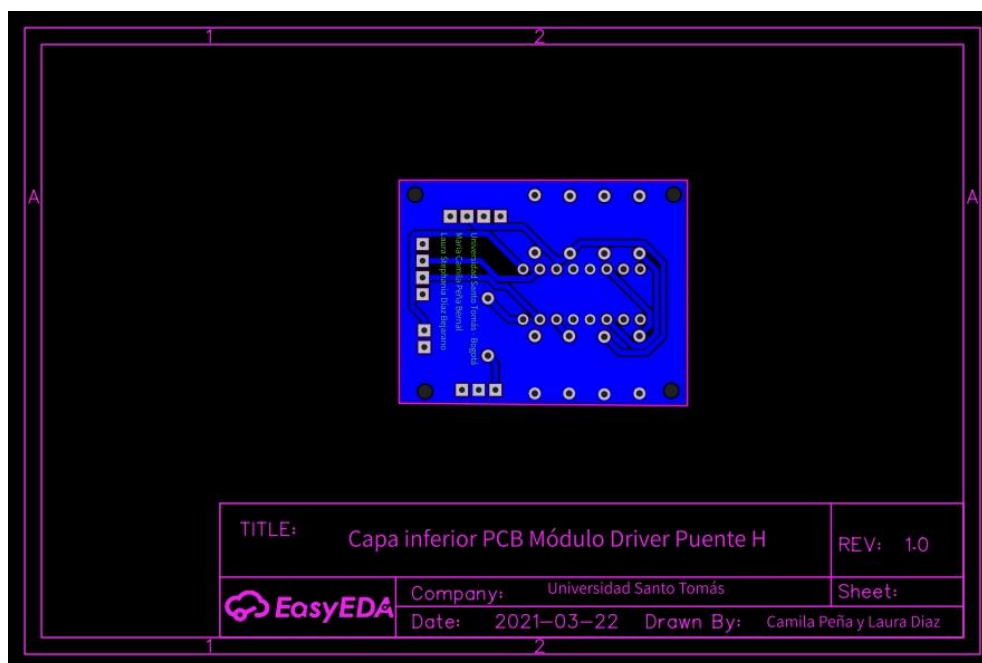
Diseño capa inferior PCB módulo Driver Puente H.
